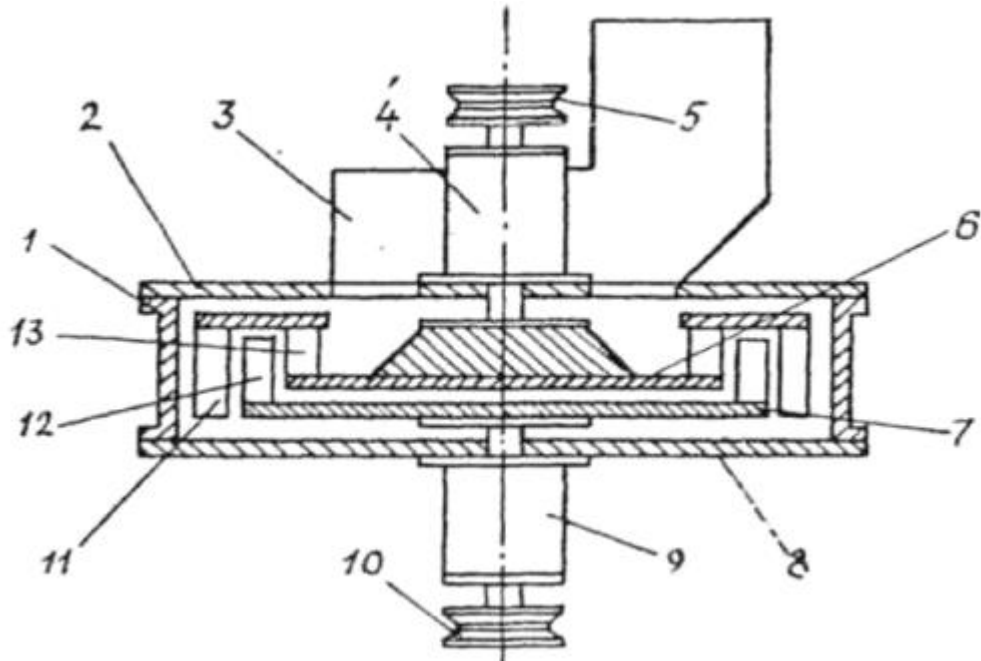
Схема ударно-відцентрової дробарки з зустрічнообертливими роторами
